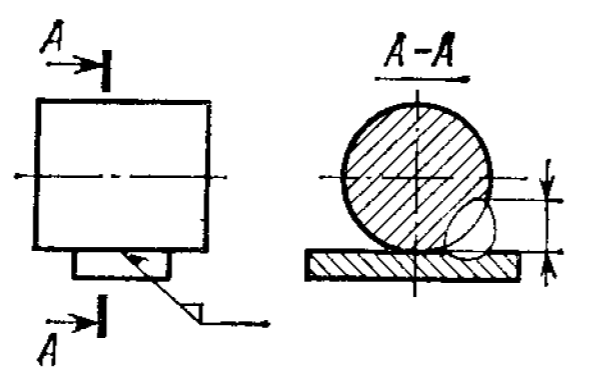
Условное обозначение одинаковых сварных швов
